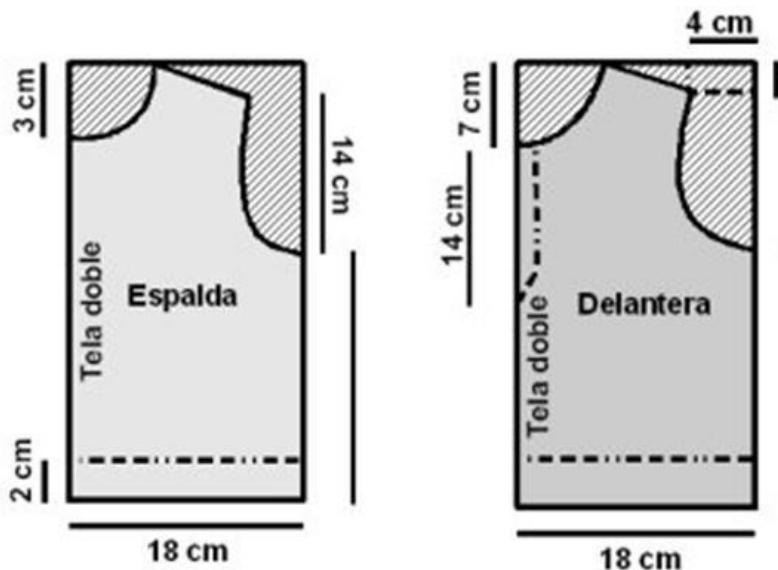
Plano de espalda y delantera. Fuente: Autoría propia.
